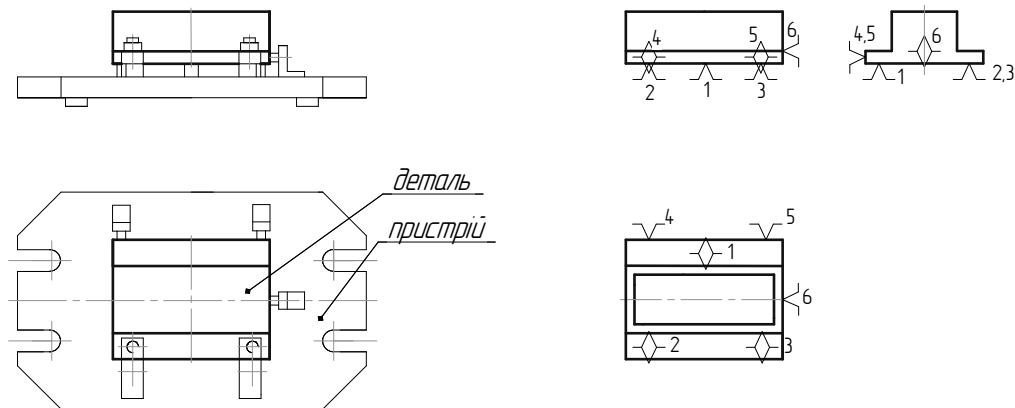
Схема базування корпусної деталі по площині основи і двох бокових поверхнях.
